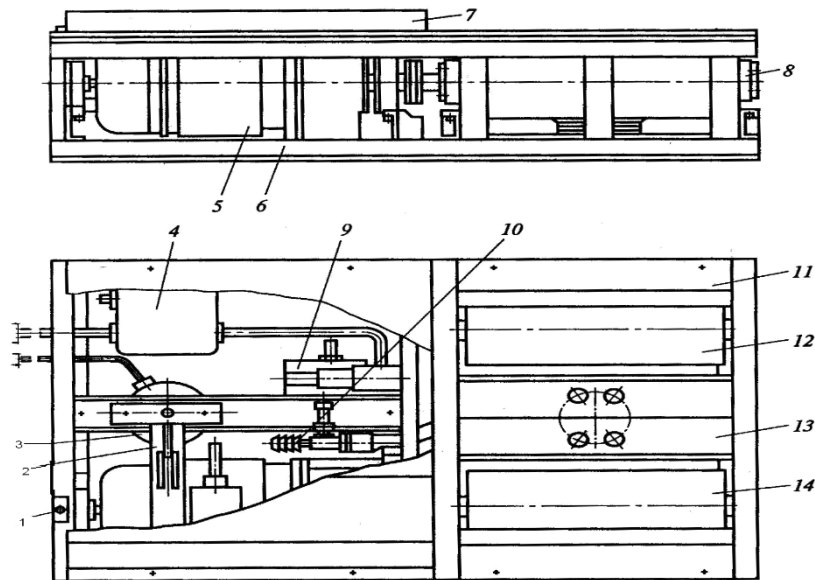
Блок роликів стенду IW-4: 1 - заземлення; 2-важіль; 3 - датчик силовимірювальної системи; 4 - клемна коробка; 5 - мотор-редуктор; 6 - рама; 7 - кришка; 8 - опори; 9 - пневморозподілювач; 10 штуцер приєднання підйомника 2-го блоку; 11- трап; 12 - підтримує ролик; 13 - підйомник; 14 - провідний ролик
